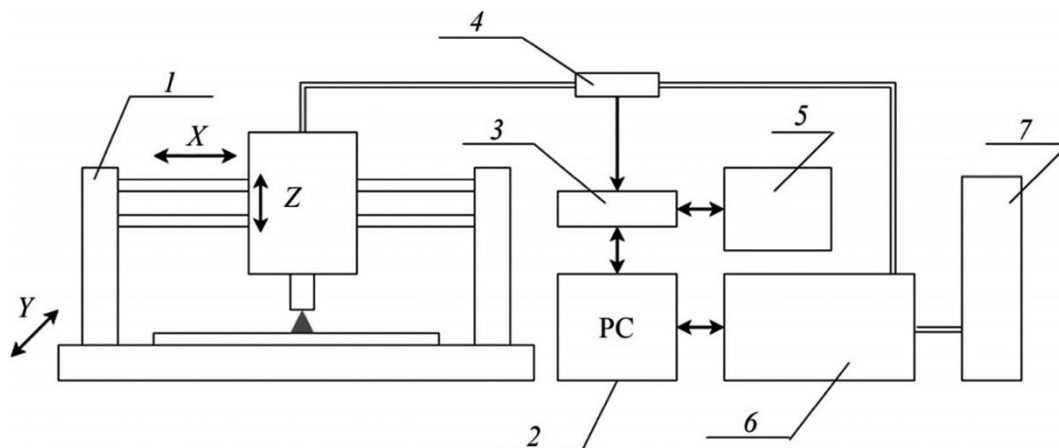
Схема экспериментального стенда WAAM на базе станка с ЧПУ: 1 — трехкоординатный станок с ЧПУ портального типа; 2 — ПК; 3 — АЦП/ЦАП; 4 — датчики силы тока и напряжения; 5 — система ЧПУ; 6 — сварочный полуавтомат; 7 — баллоны с защитным газом
